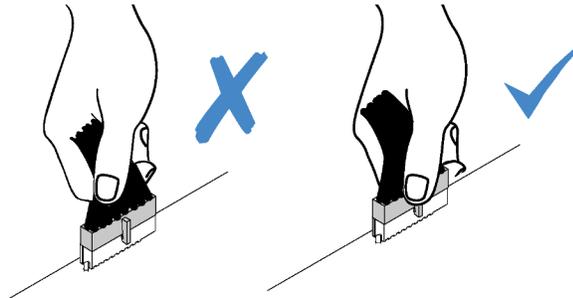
Desconexión de los cables del módulo de alimentación flash RAID
